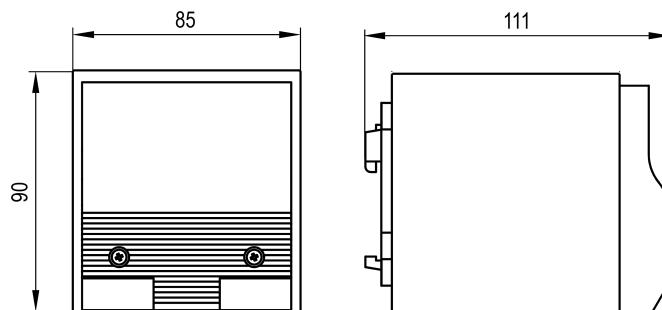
Габаритные размеры МТК-ЕFxxx
